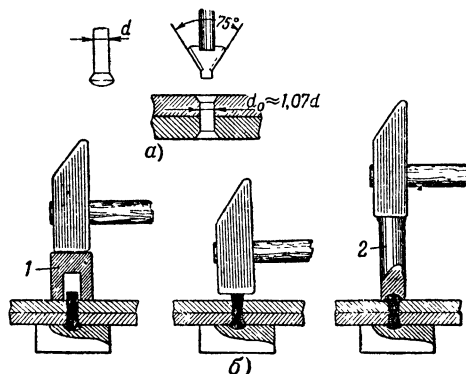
Заготовка отверстия под заклепку (а) и открытая клепка (б).
